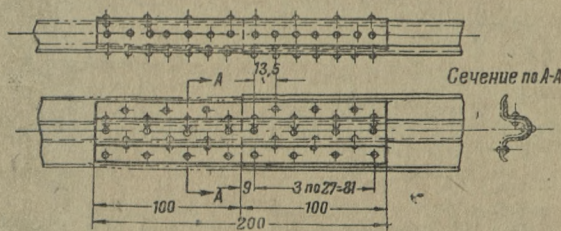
Стыковка профильного лонжерона или стрингера с лапками по размерам профиля
